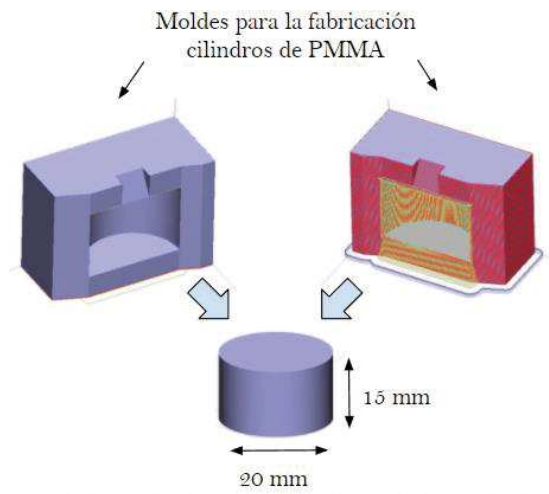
Moldes diseñados para la construcción de cilindros de PMMA
